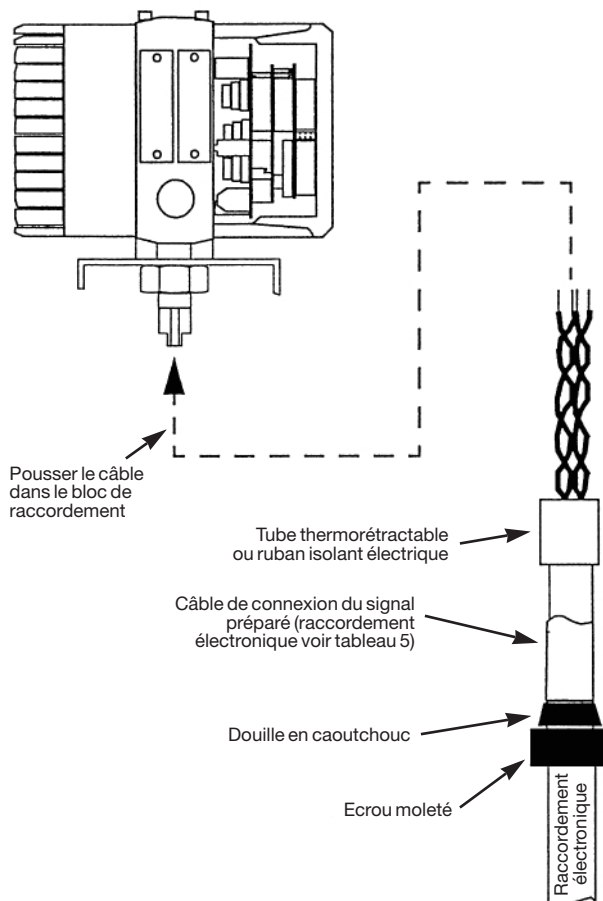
Vue d'ensemble du VFM 3100 à montage séparé
